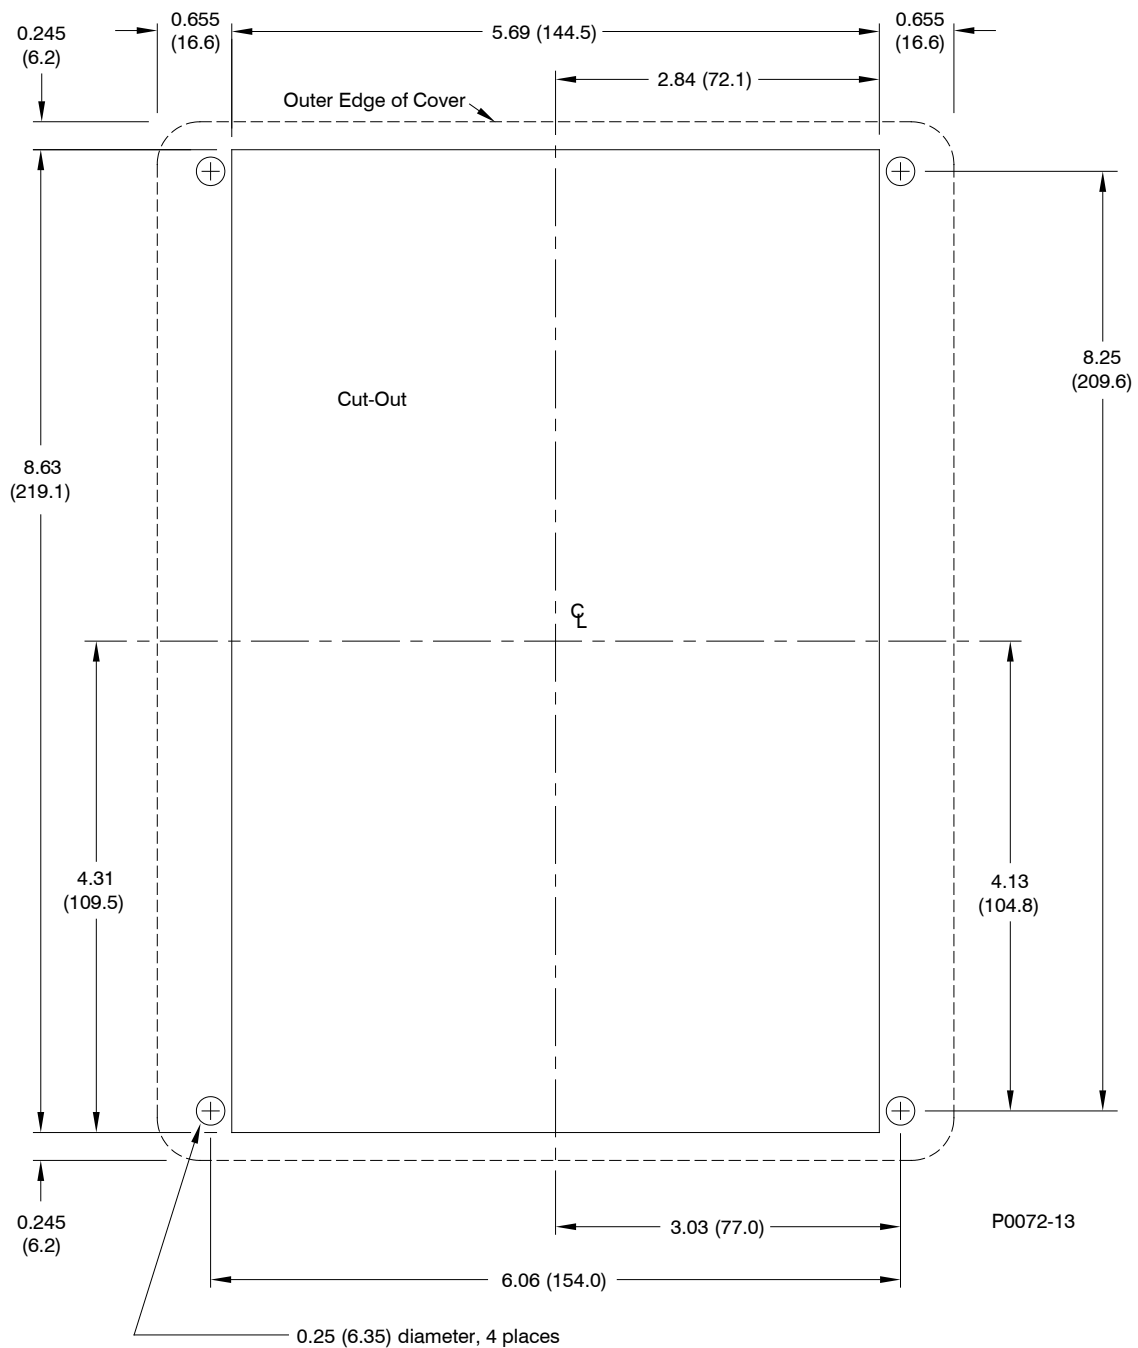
Boîtier de type J - Dimensions de perçage et de découpe
